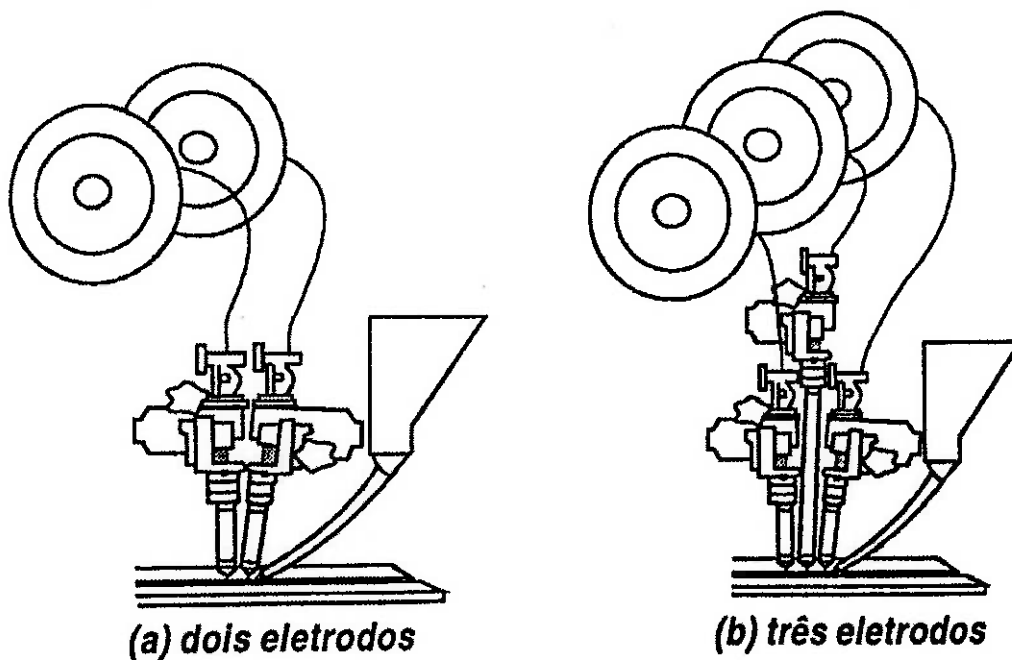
a) Disposição típica para soldagem Tandem-Arc com dois arames.
